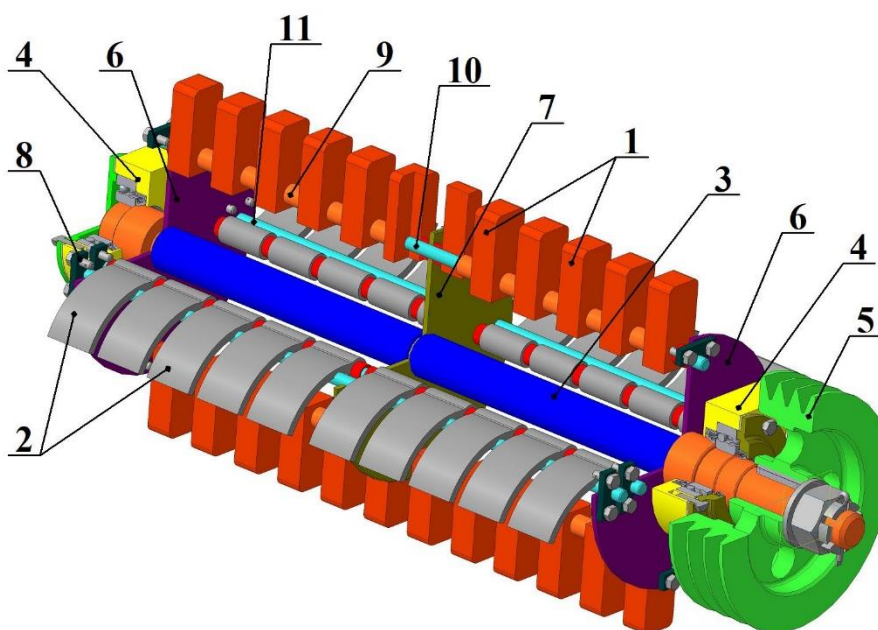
Схема комбинированного ротора с дробящими бойками и скалывающими лопатками
